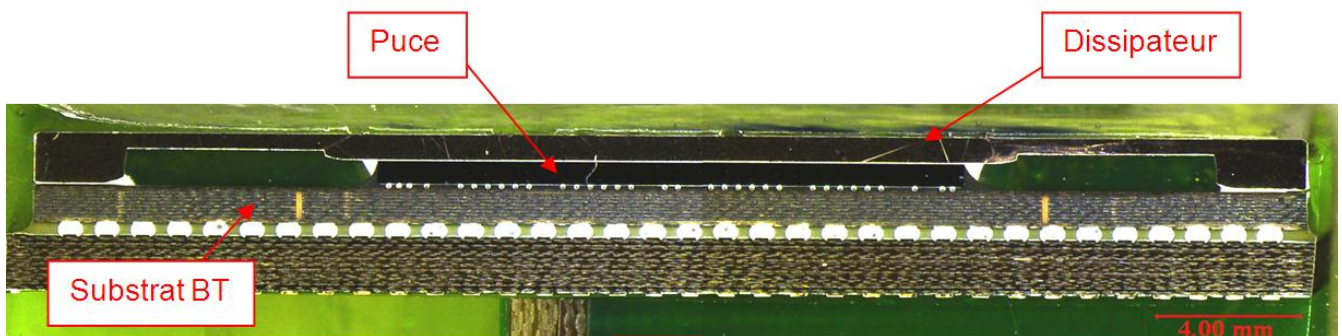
vue en coupe d'un BGA Xilinx 1152
